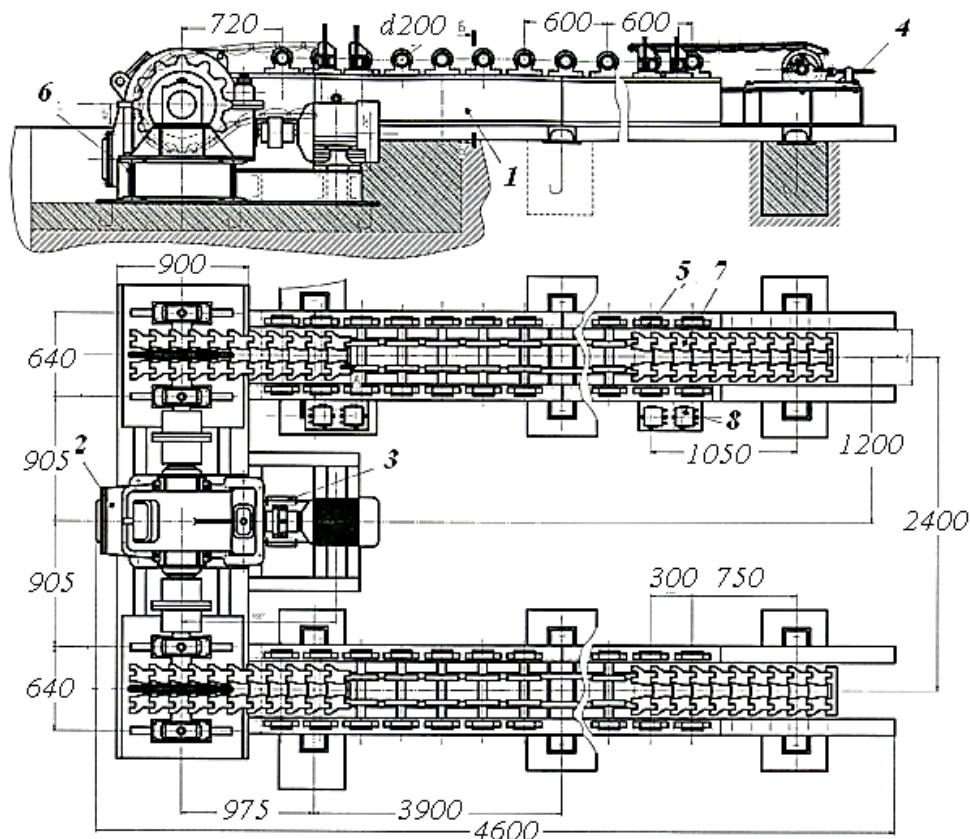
Общий вид тракового конвейера: 1 – став; 2 – привод конвейера; 3 – кожух кулачковой муфты; 4 – натяжная станция; 5 – роликовая опора; 6 – рама привода; 7 – трак (звено гусеницы); 8 – установка конечных выключателей
